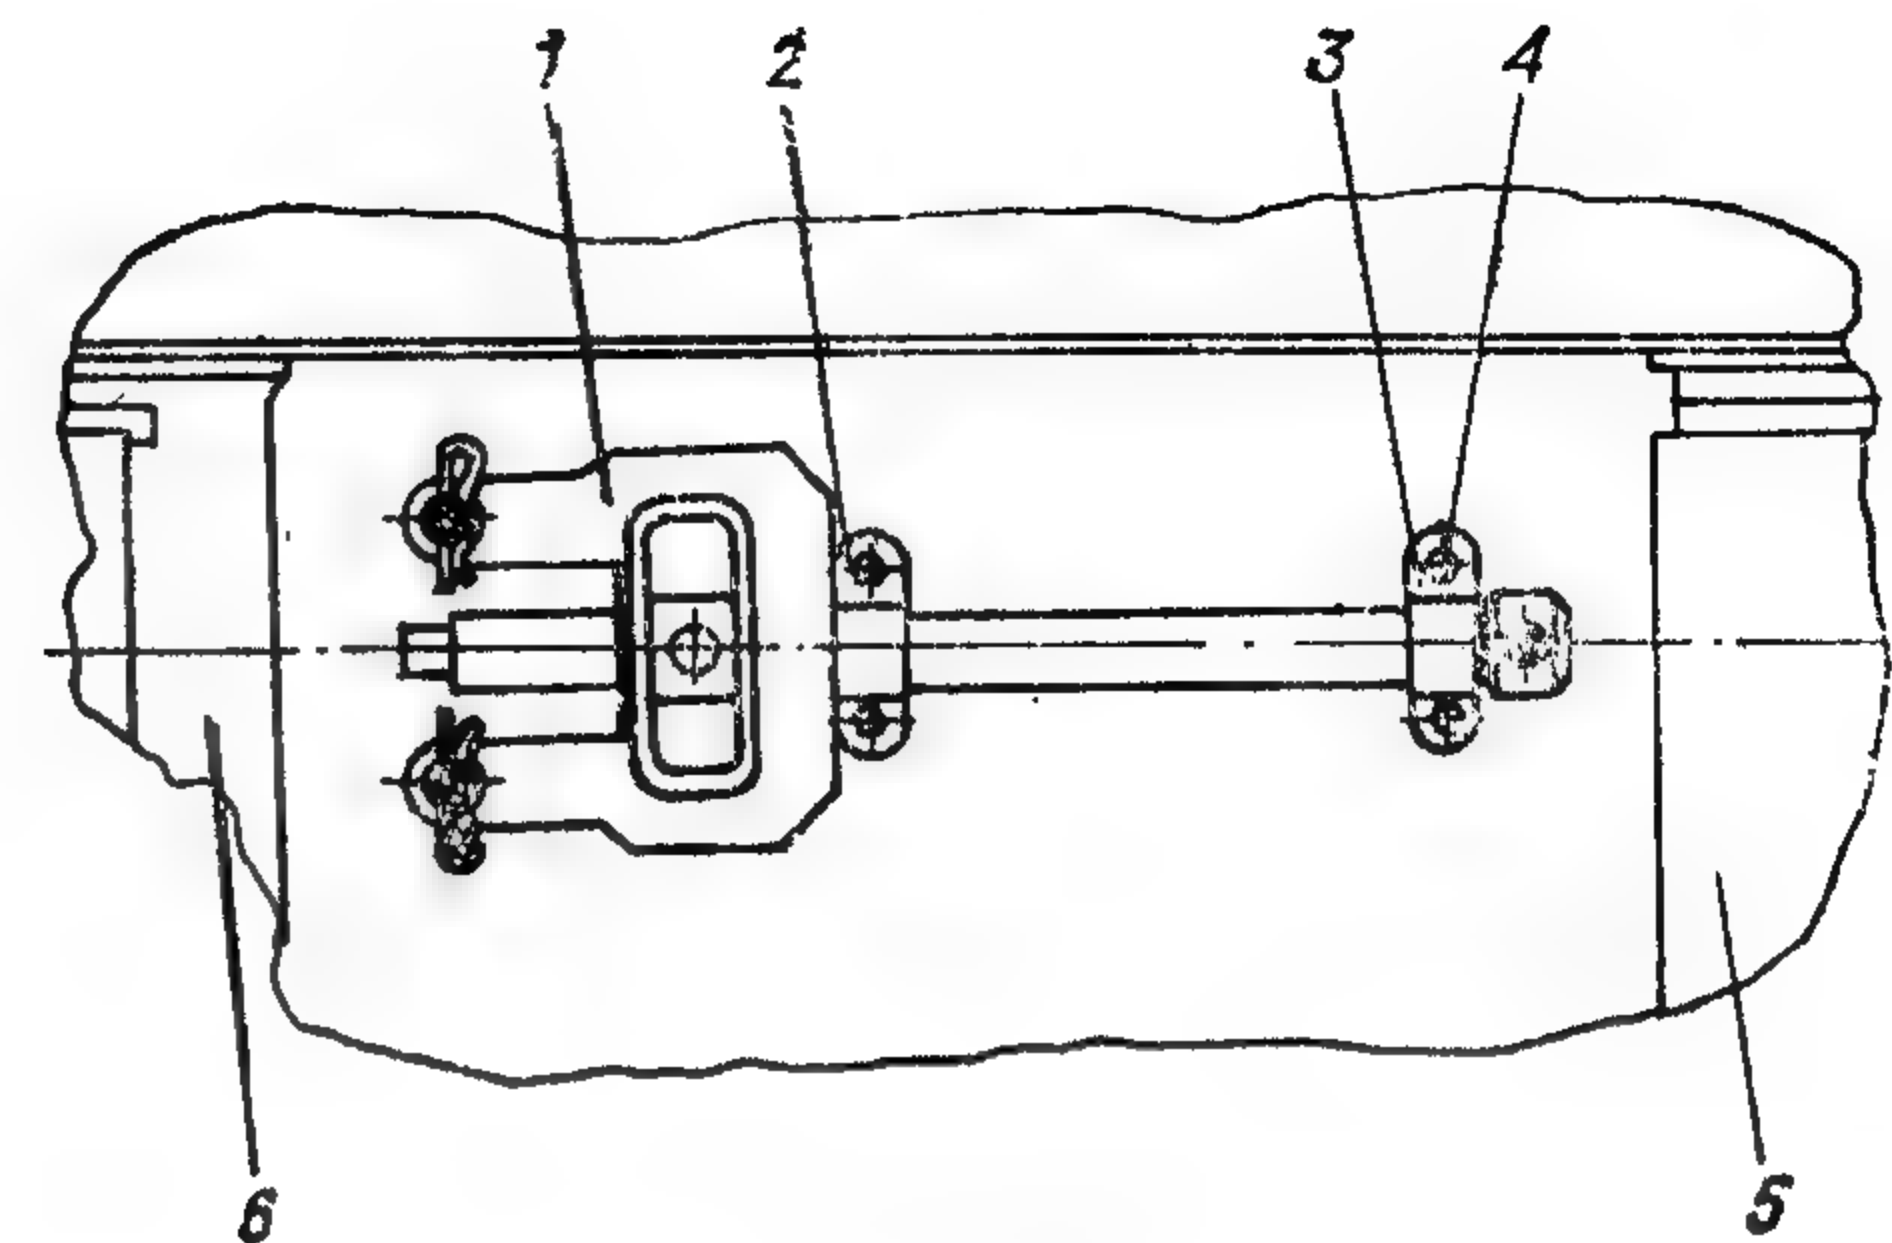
Установка приспособления для выпрессовки пальцев гусениц:
